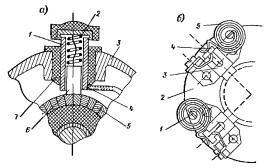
Щеткодержатели малык машин: a — трубчатый  $\delta$  — коробчатый
